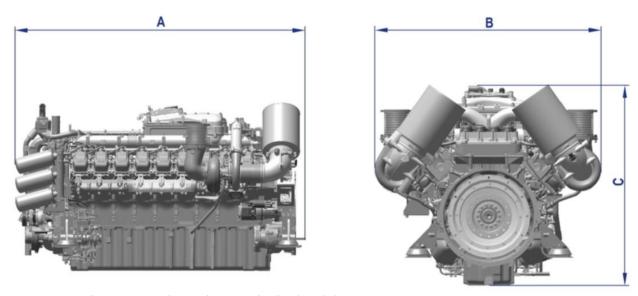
Dimensiones principales del motor MTU 16V 2000G26F [11].
